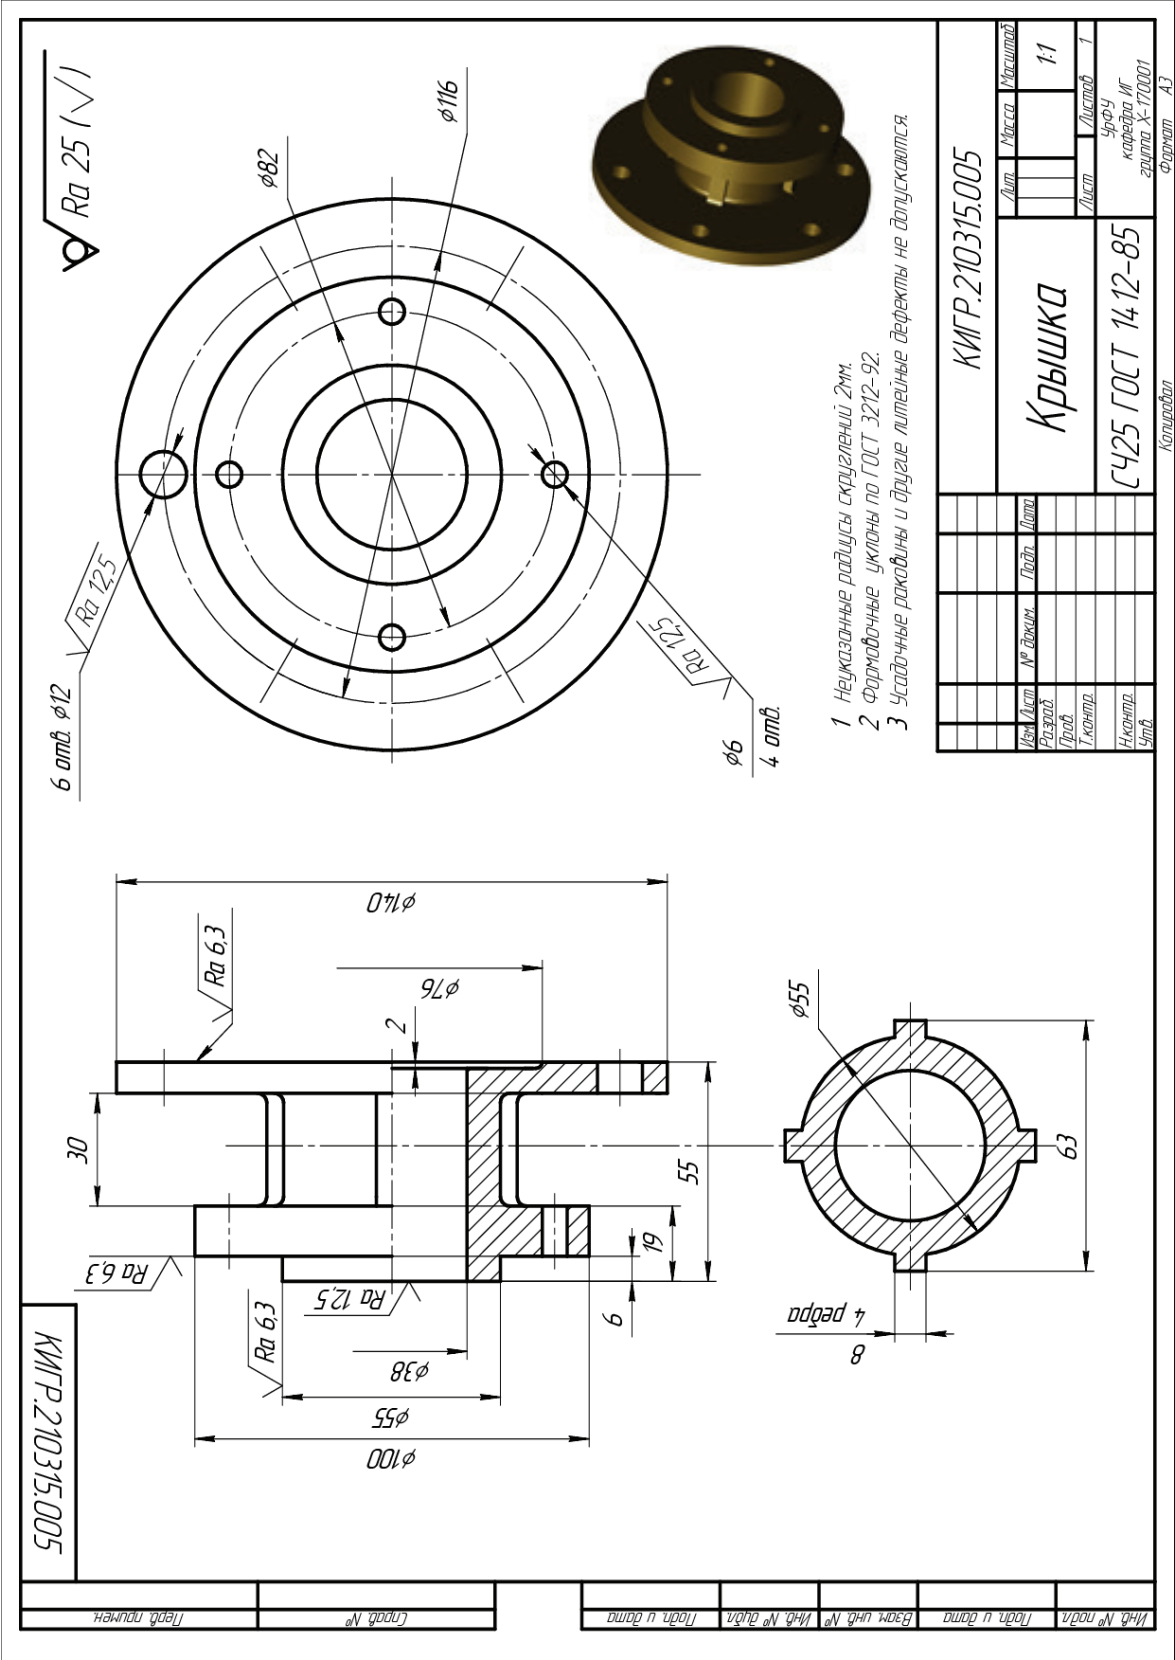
Пример учебного чертежа литой детали «Крышка»
